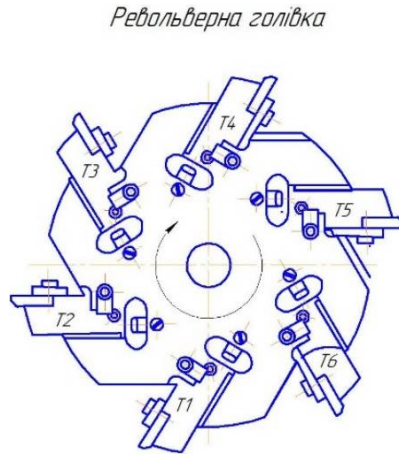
схема закріплення ріжучого інструменту у револьверній голівці
